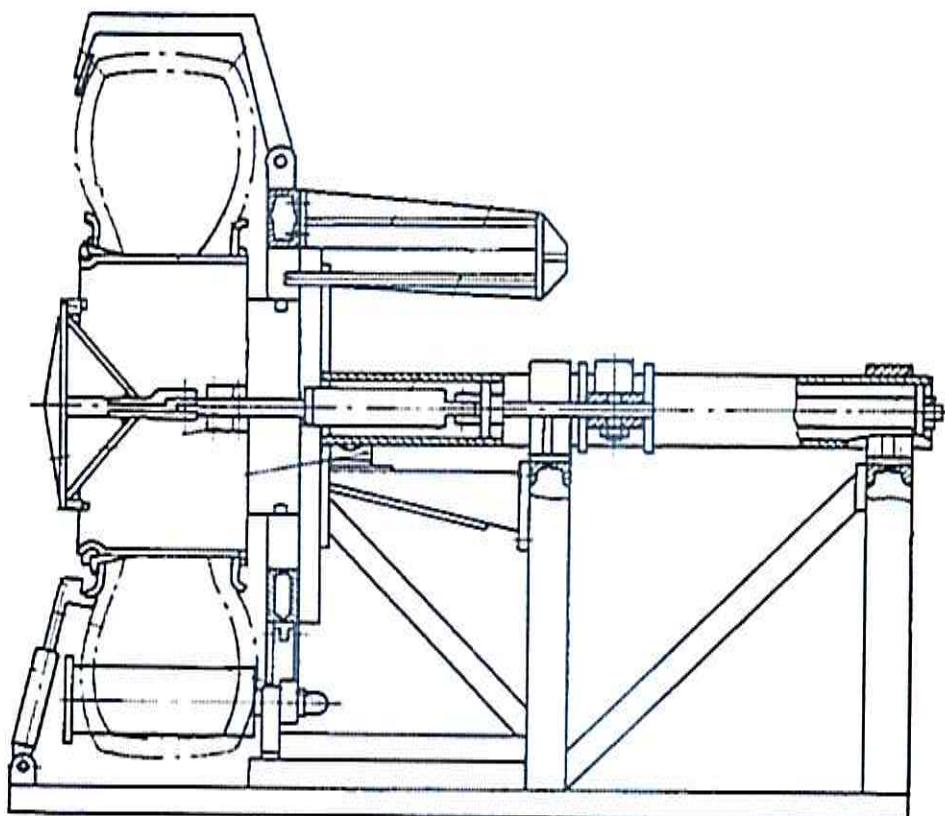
стенд для демонтажа и монтажа шин
